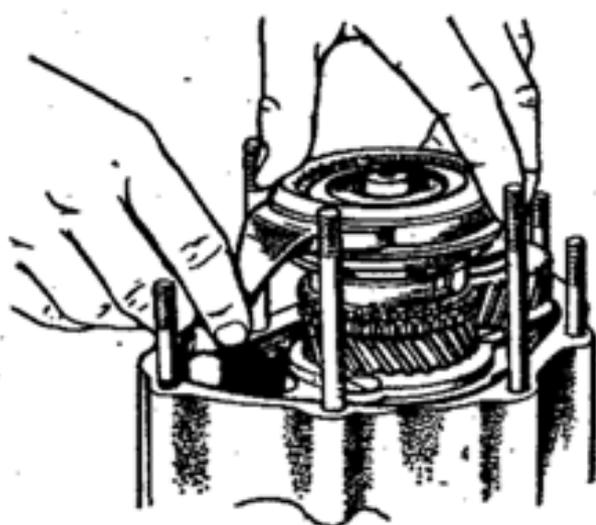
Снятие муфты, ступицы и вилки пятой передачи
